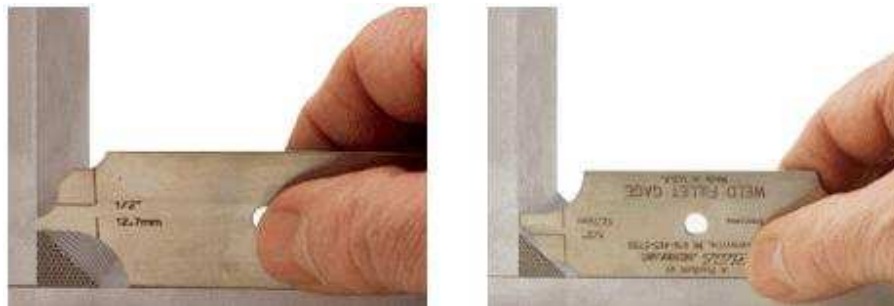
Calibrador de soldaduras de filete.
